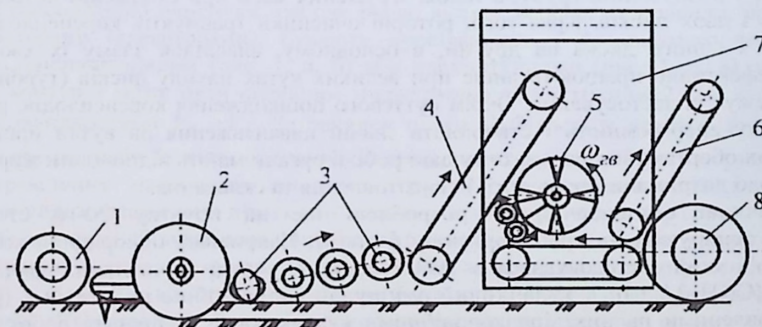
Конструктивно-компоувальна схема модернізованої коренезбиральної машини: 1 – копіювальне колесо; 2 – дисковий сферичний копач; 3 – очисник вороху; 4, 7 – повздовжній і вивантажувальний транспортери; 5 – транспортерно-гвинтовий очисник; 6 – гірка; 8 – опорне колесо.
